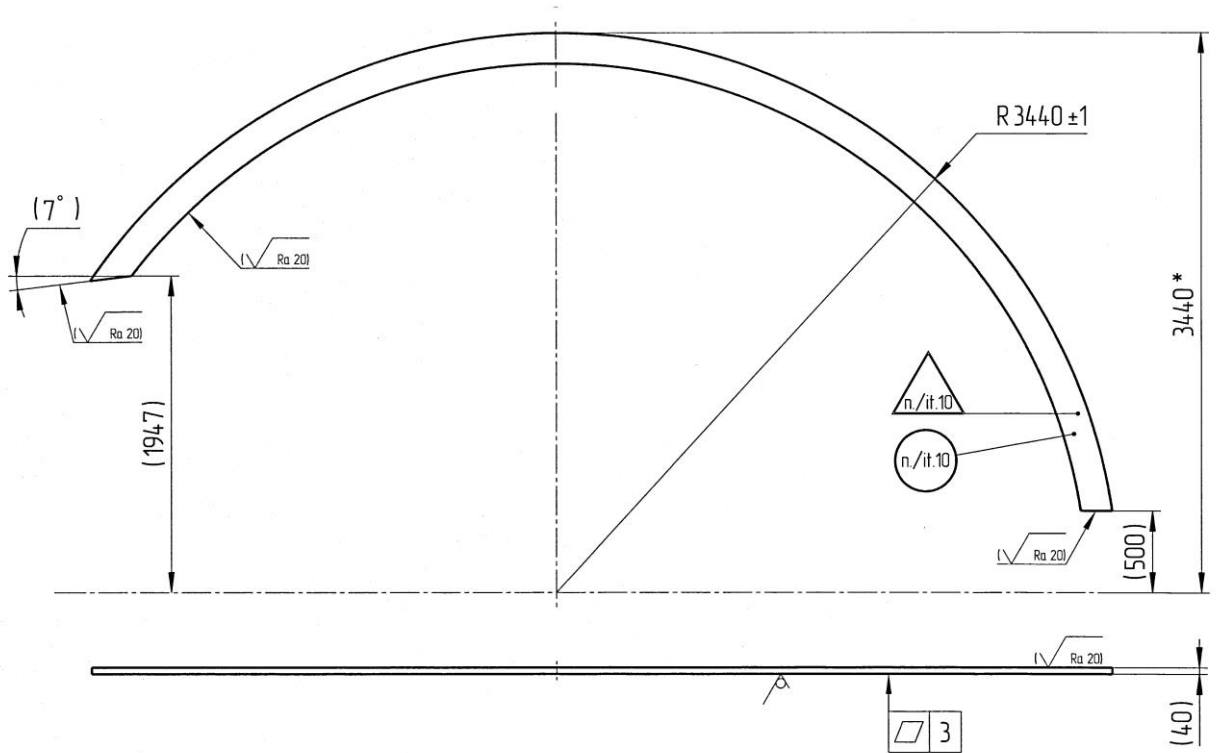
Заготовка полукольца опоры толщиной 40 мм
